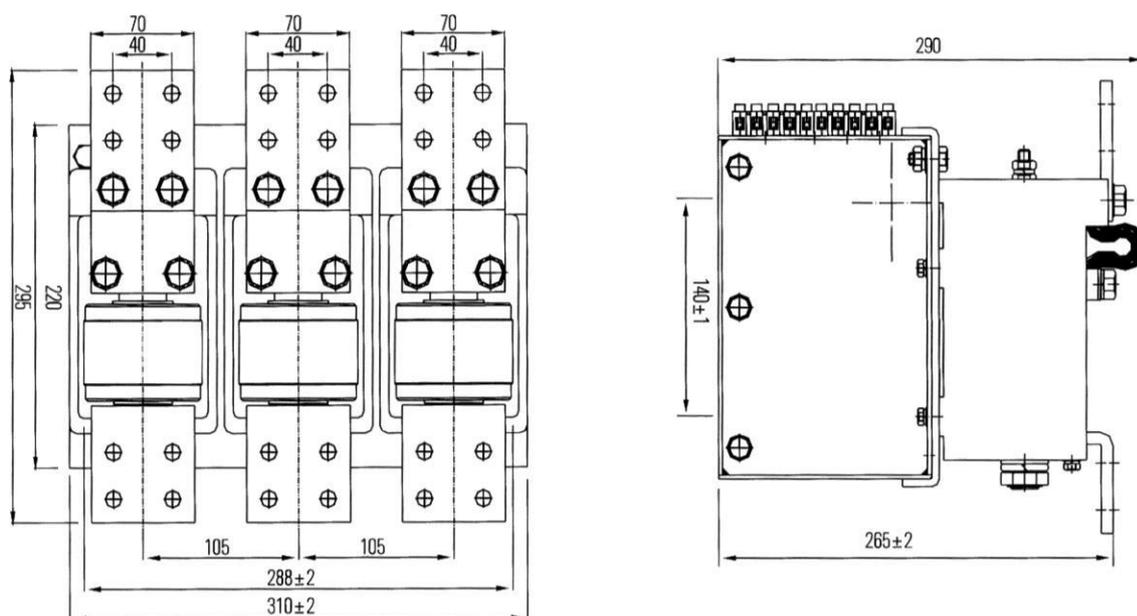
Габаритные размеры КВТ-1,14-1000/1250
